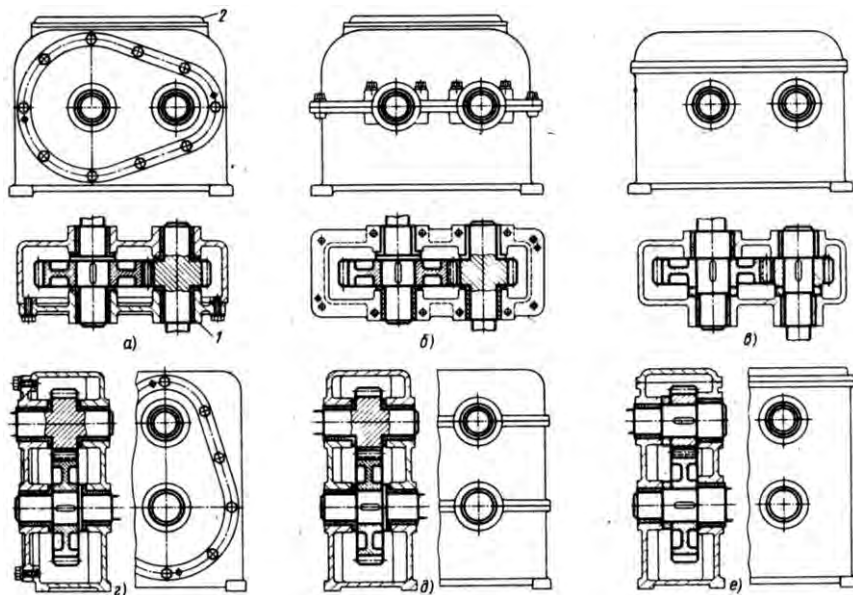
Схемы сборки одноступенчатых редукторов
